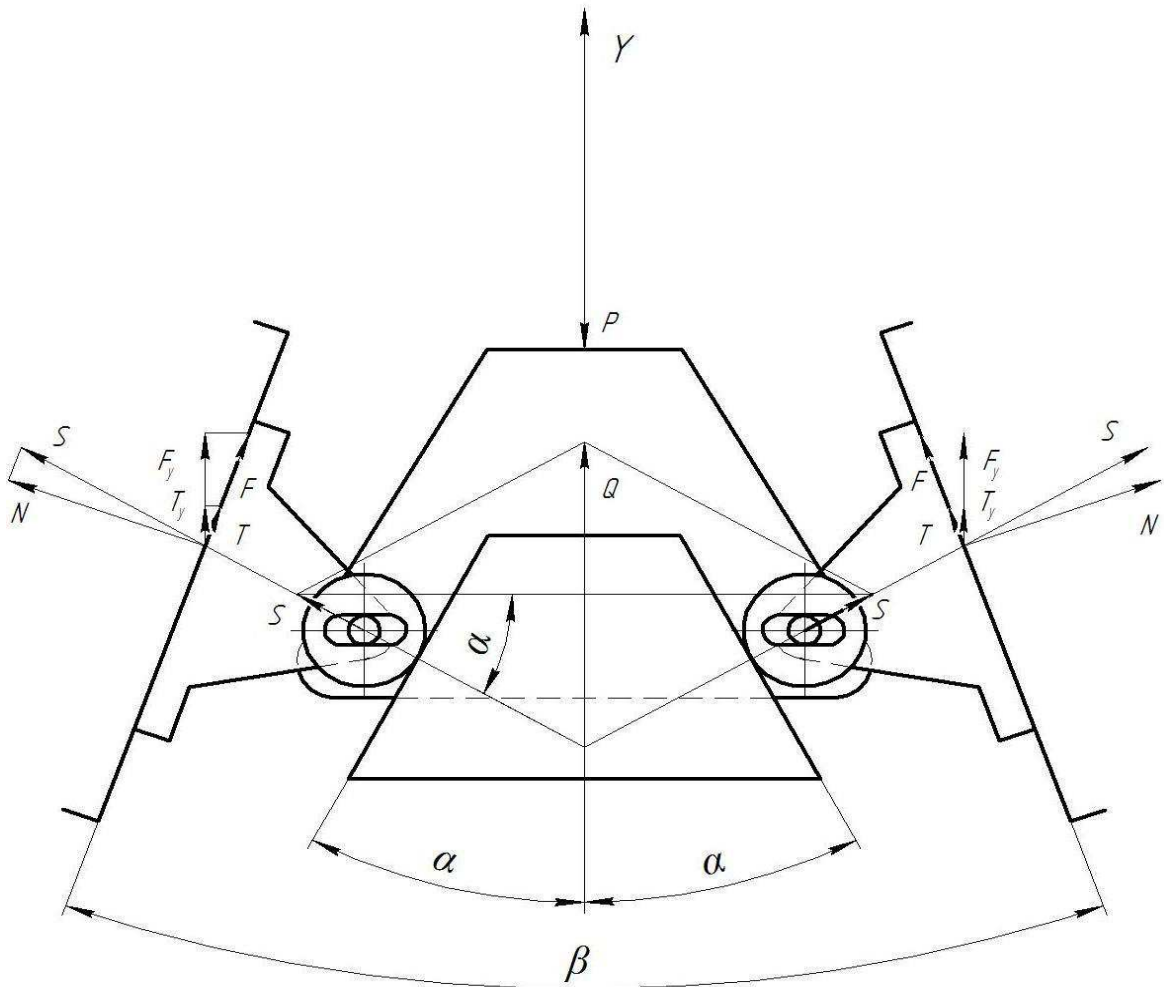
Розрахункова схема фрикційної виливниці
